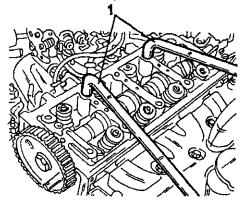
Поднимание головки цилиндров с помощью двух рычагов (1).
